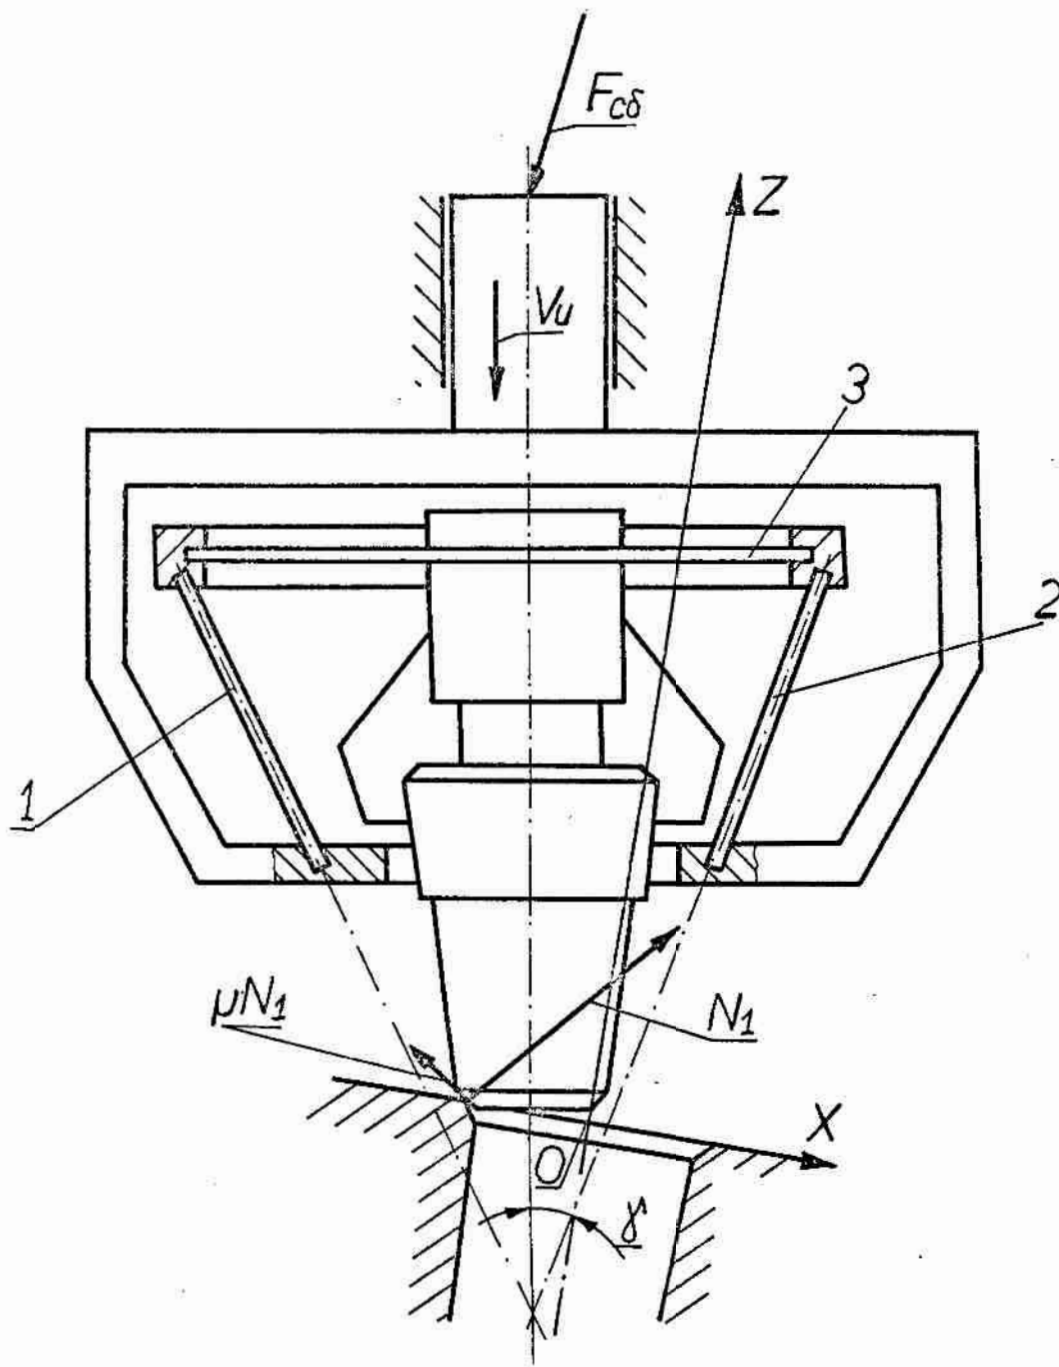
Сборочное устройство с упругими базирующими элементами
